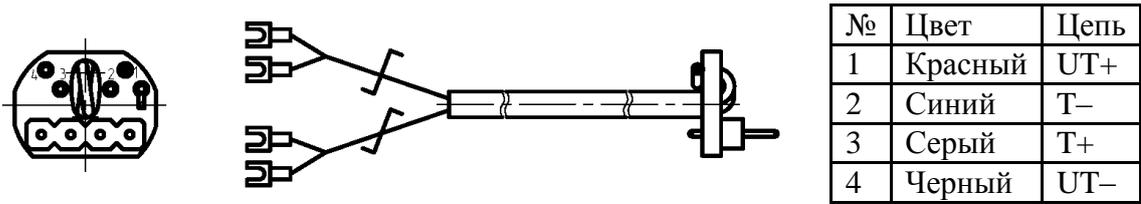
Соединитель канала T1 (006.104.000)
